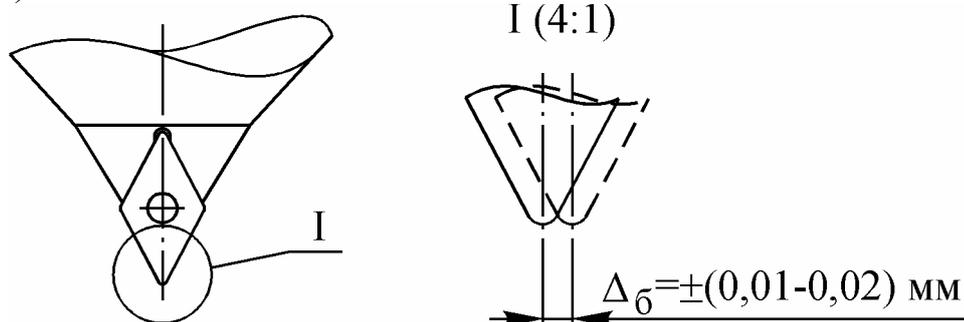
Погрешность базирования резцовой головки во фрезерном шпинделе
